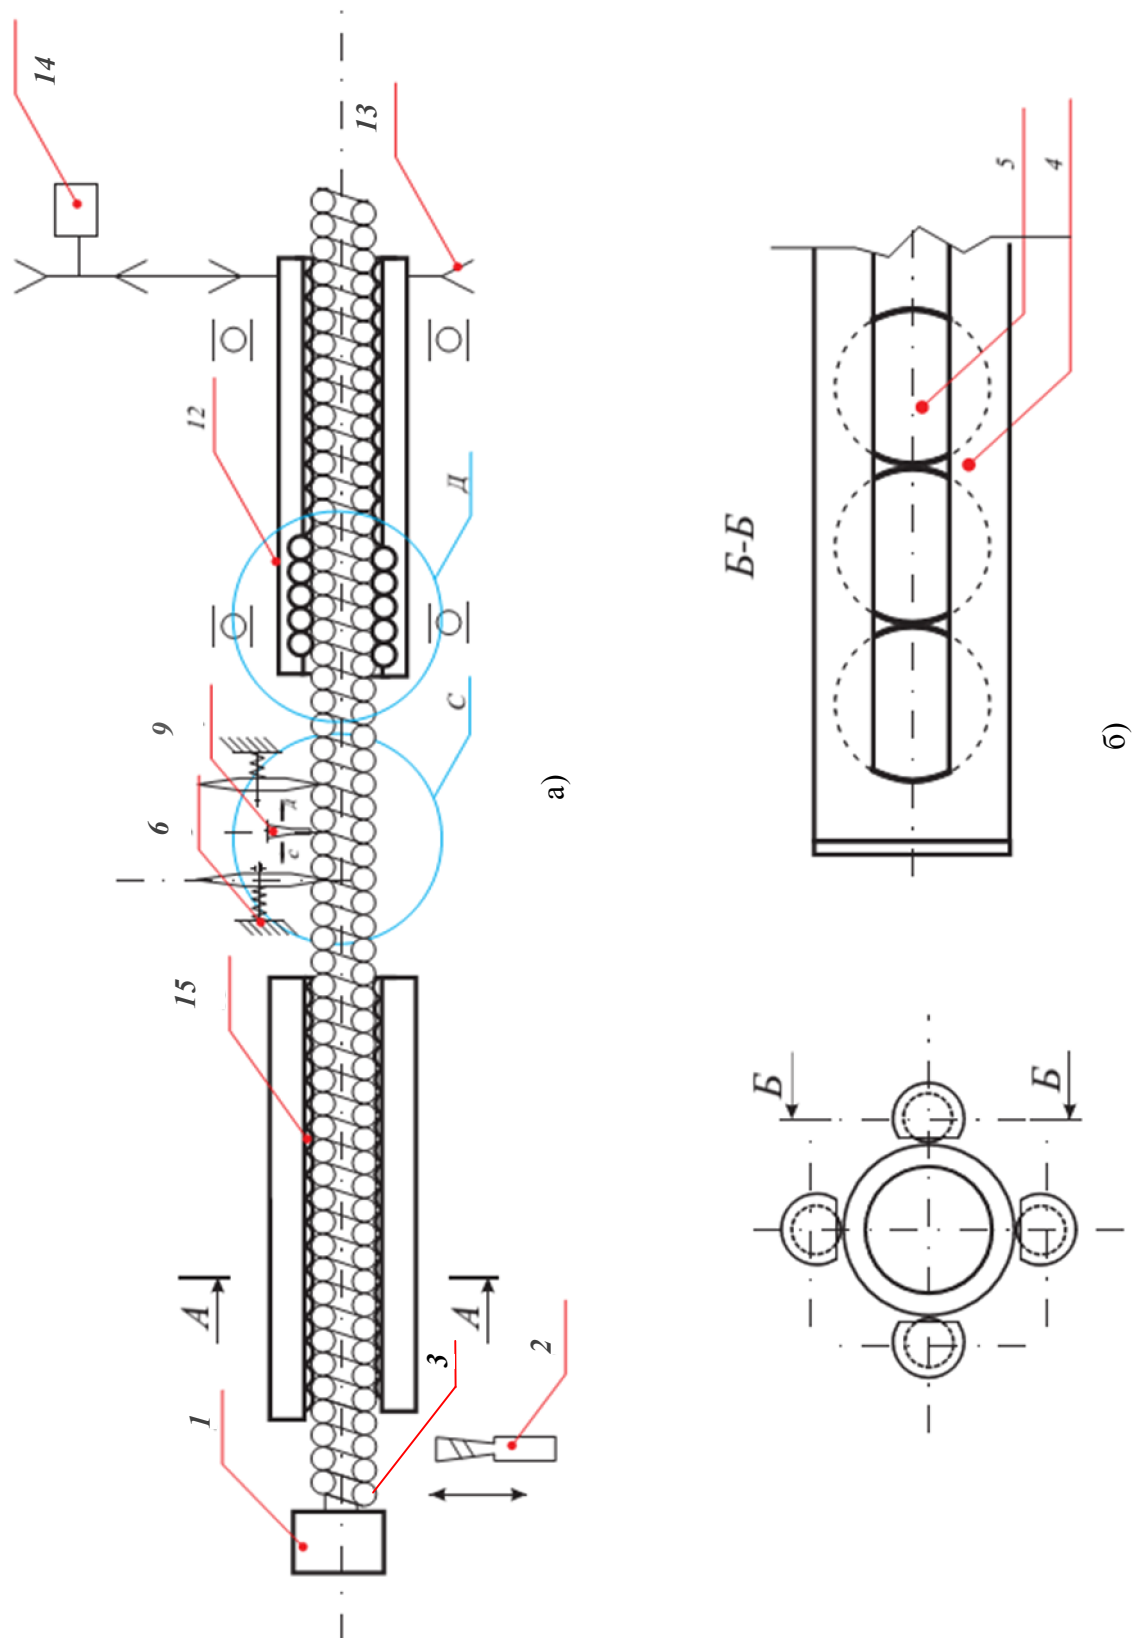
Установка лазерной сварки пружинно-витых труб:
